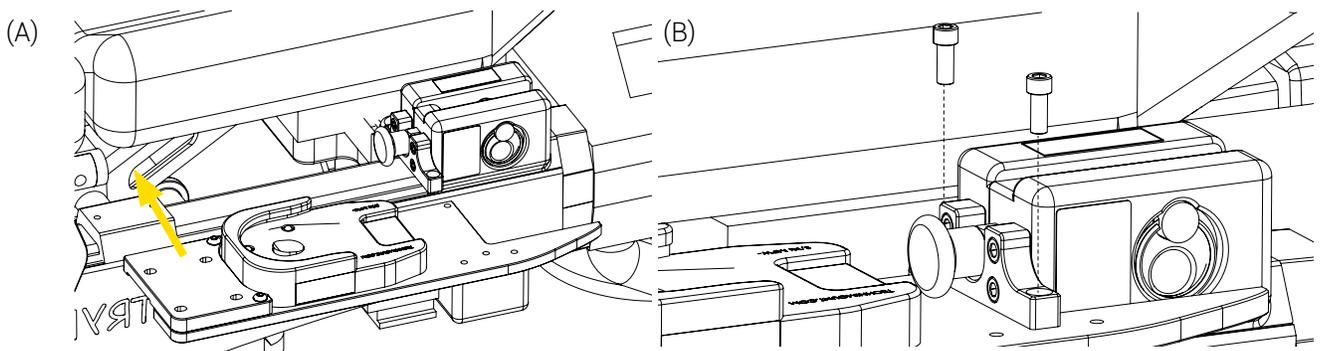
Installation de la plaque de support du IV Pro Adapter 2-SMDT
